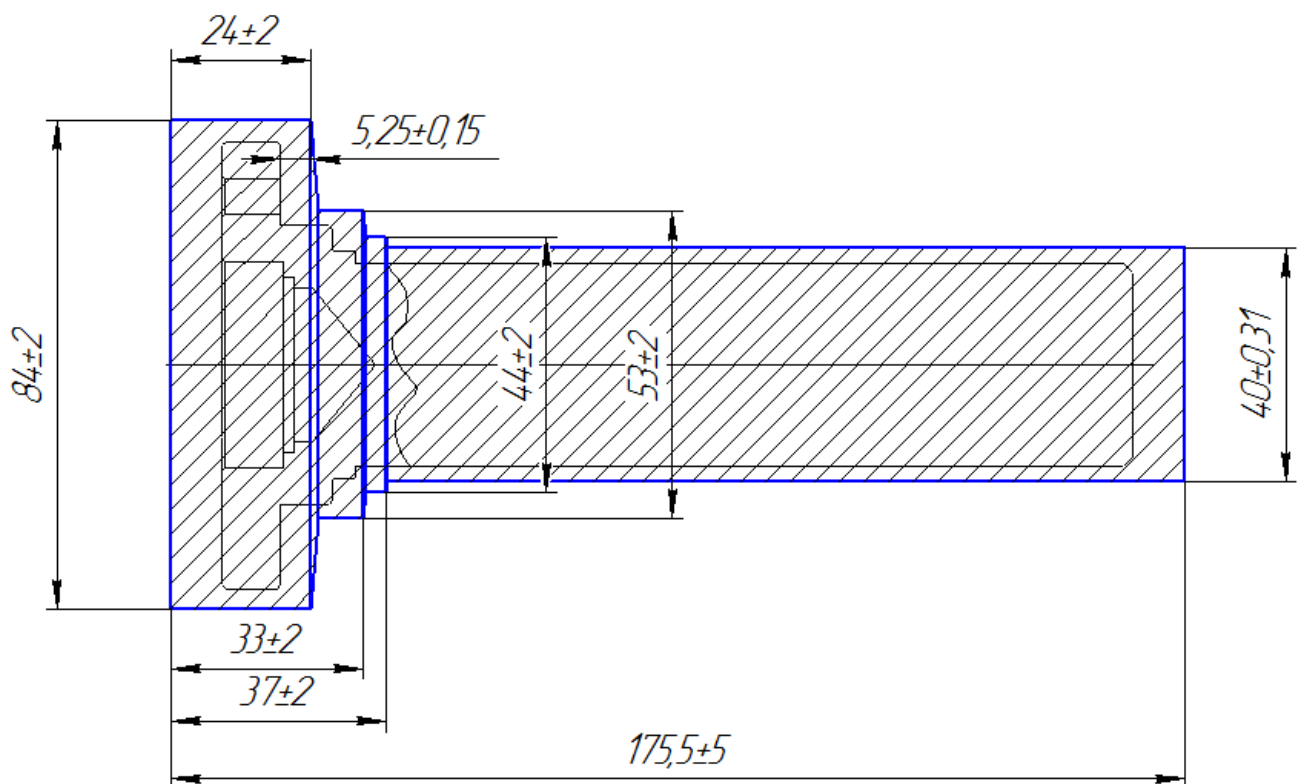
Ескіз заготовки отриманої куванням кованки
